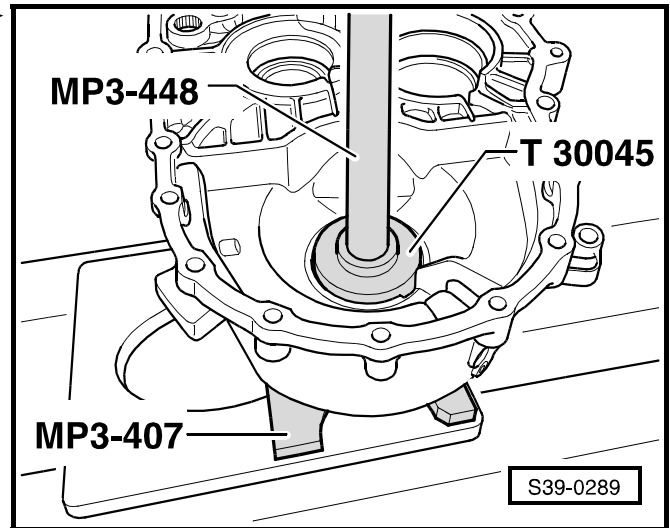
Извлечение внутреннего кольца конического роликоподшипника ►
